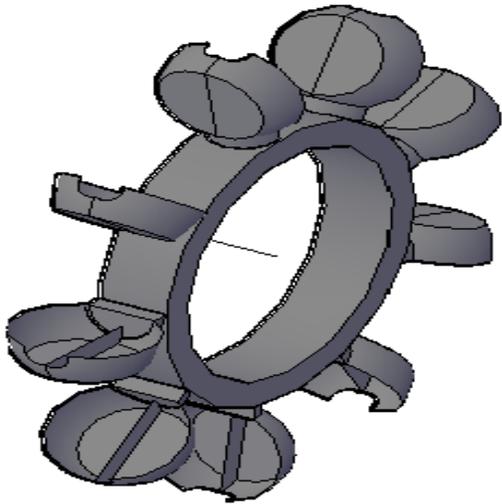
Diseño del rodete y turbina en AUTOCAD.
